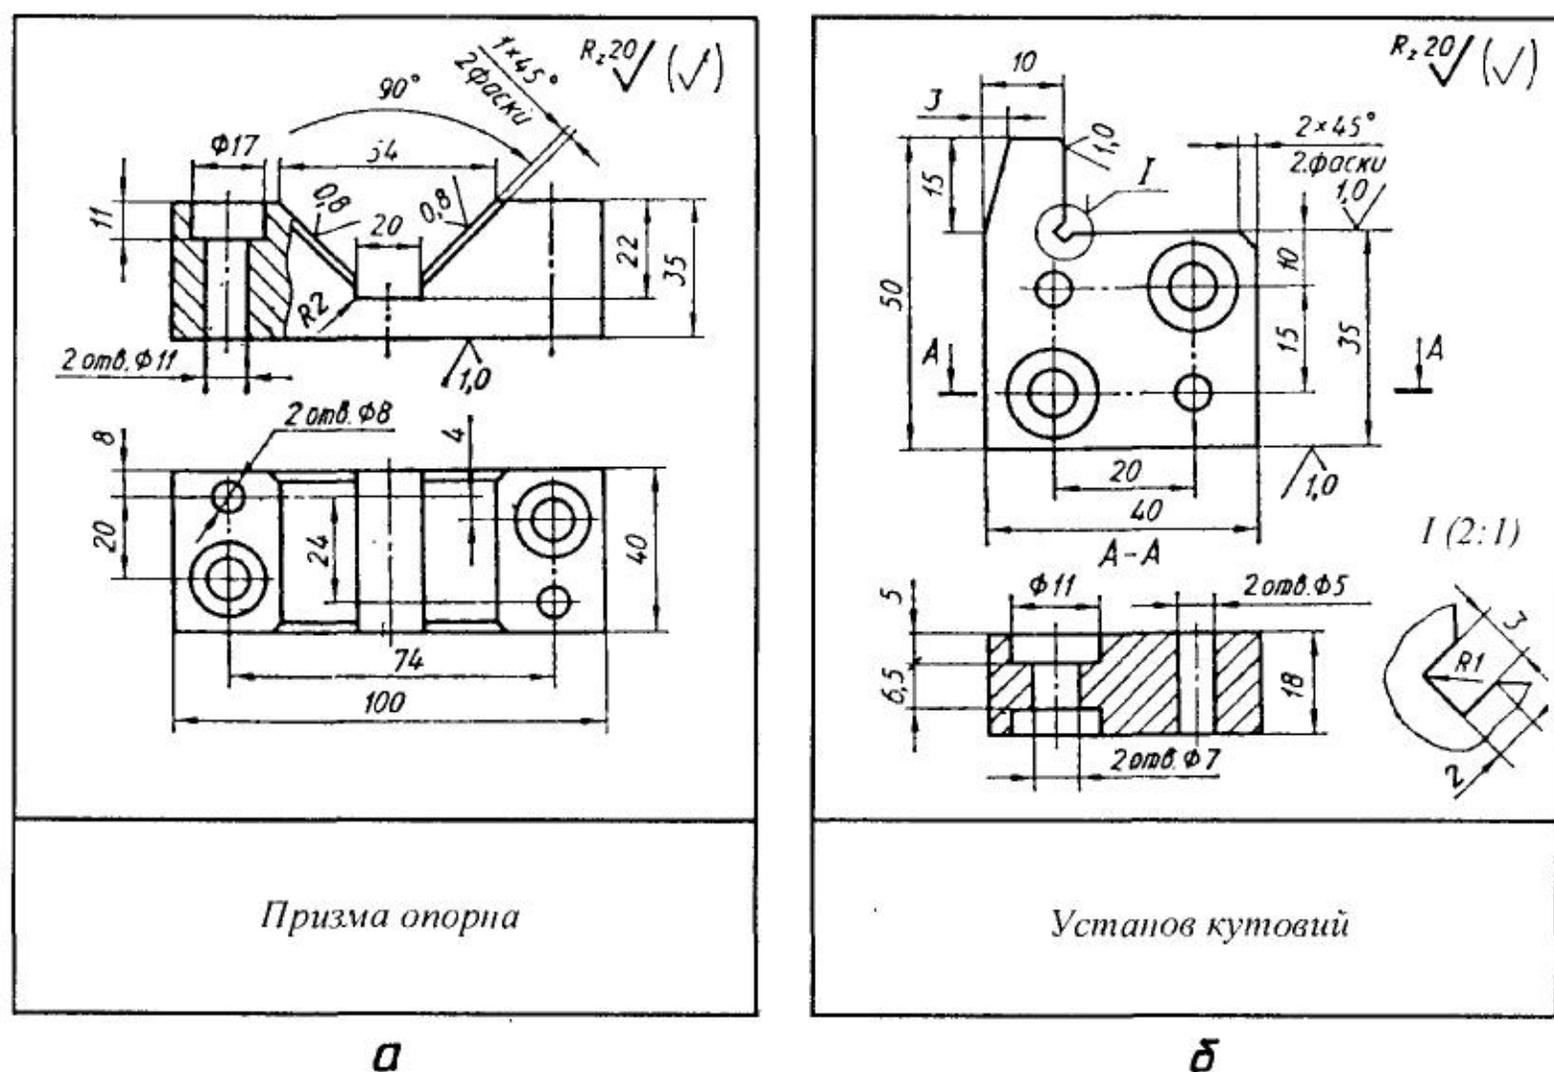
Креслення опорної призми (а) і кутового установка (б), обмежених переважно плоскими поверхнями.
